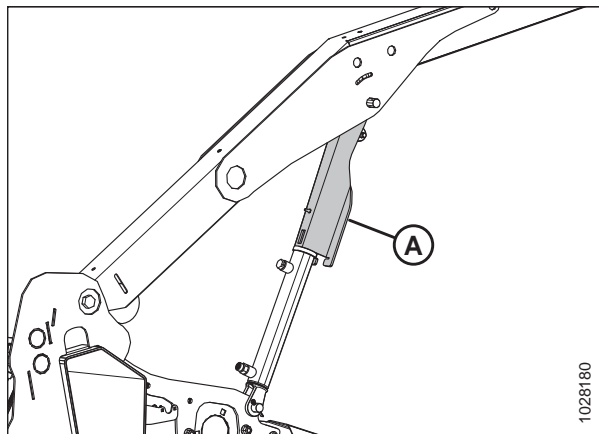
Зафиксированный предохранительный упор мотовила — правый внешний рычаг
